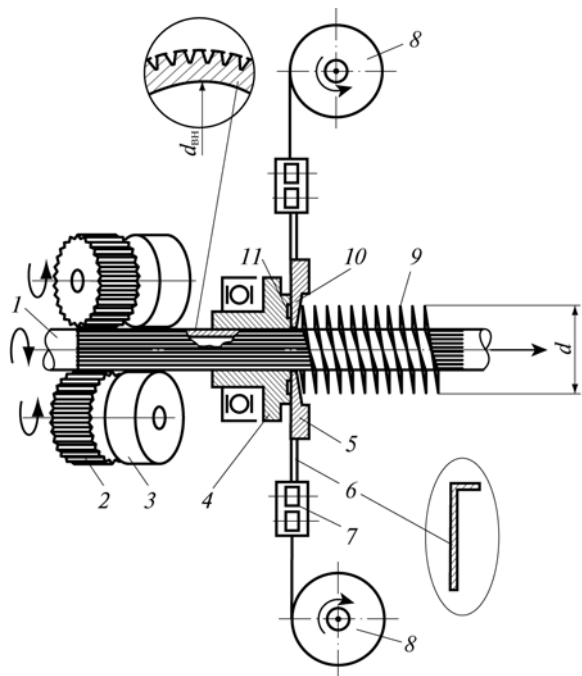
Процесс изготовления БРТ с рифлением грибовидной формы
